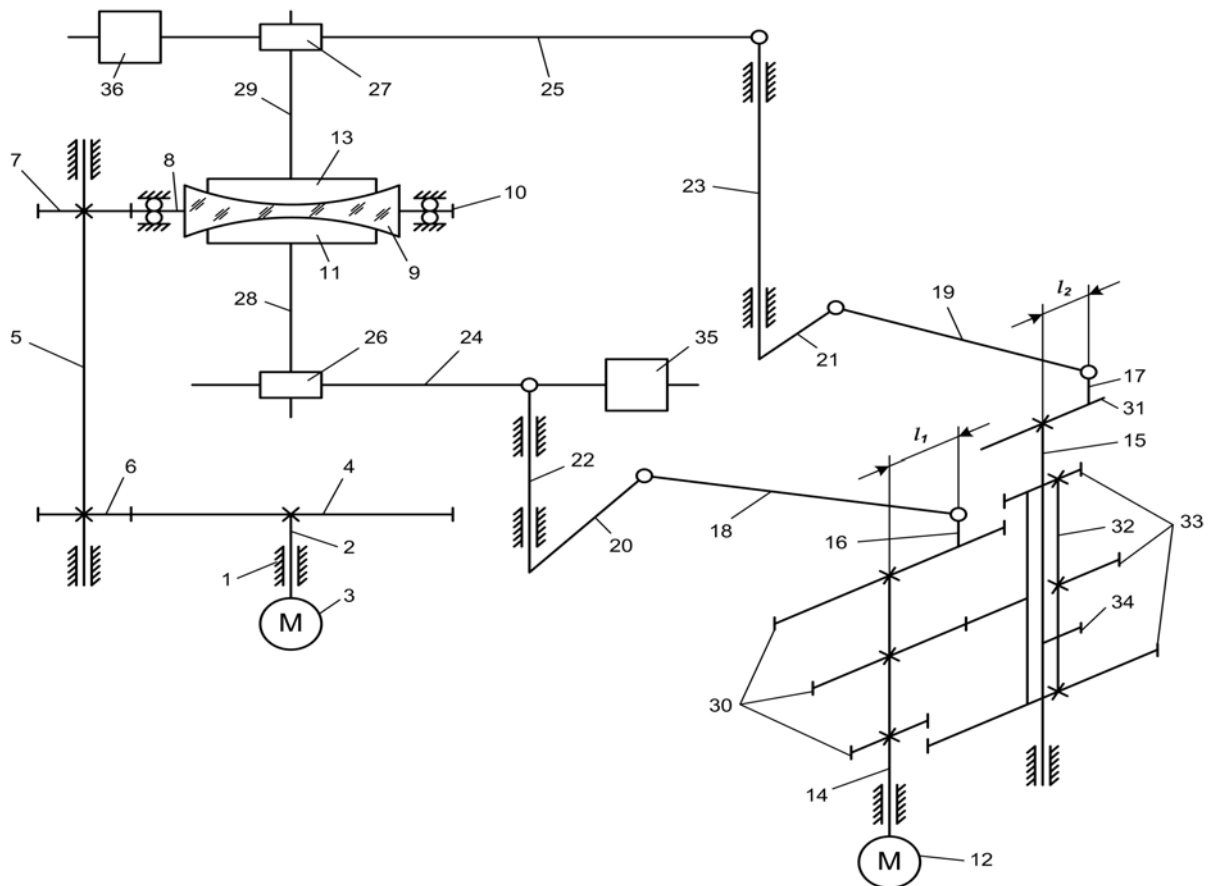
Схема станка для одновременной двусторонней обработки линз с пологими вогнутыми поверхностями
